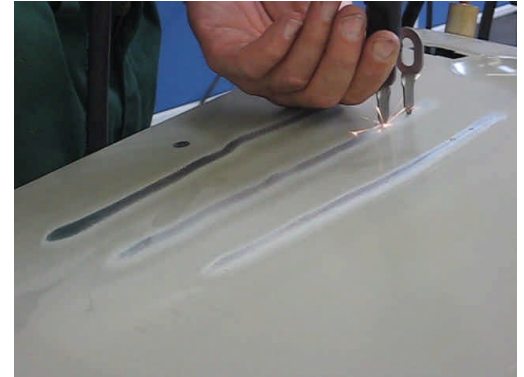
Aufschweißen der Bits (Probeblech)
